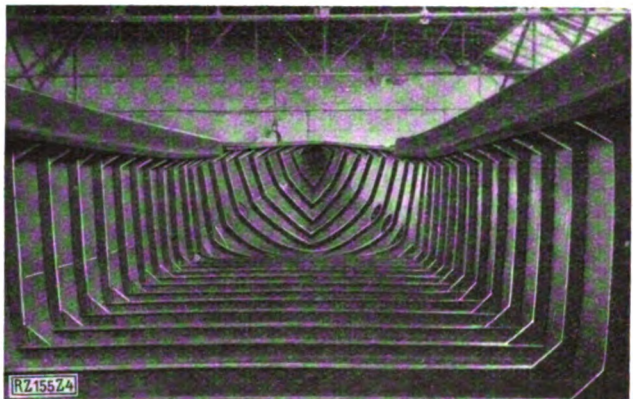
Innenansicht des fertig geschweißten Kähnes.
